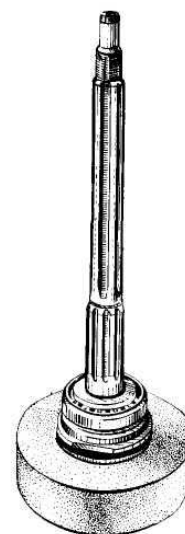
Спрессовка конического подшипника с ведущей шестерни главной передачи
